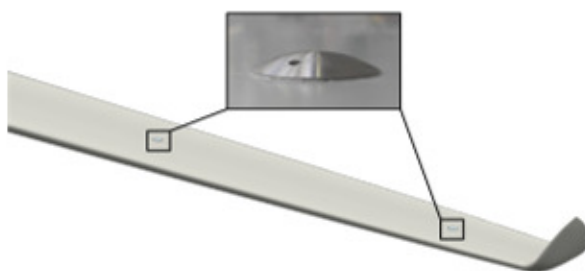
Rotorblatt mit Rezeptoren auf der Druck- und Saugseite, Beispiel
